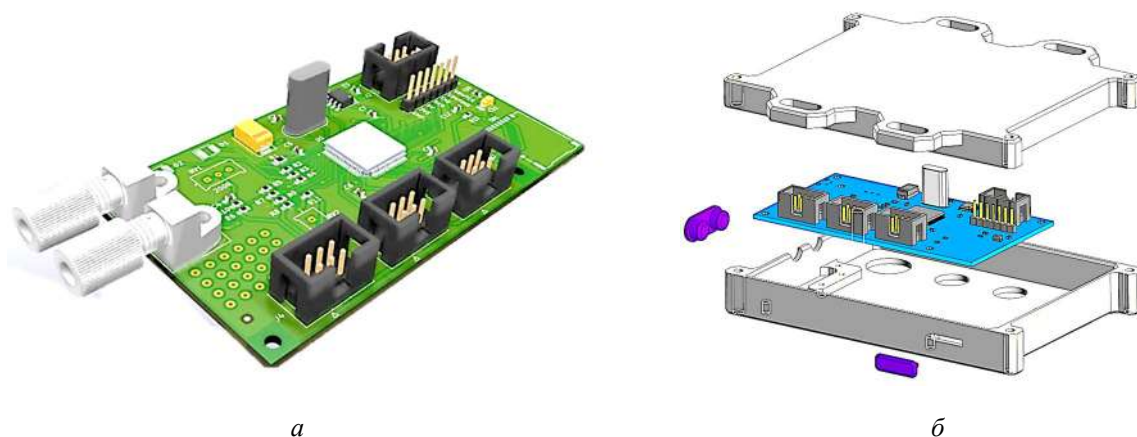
3D-визуализация размещения основных компонентов печатной платы (а) и чертеж сборки корпуса устройства (б)
